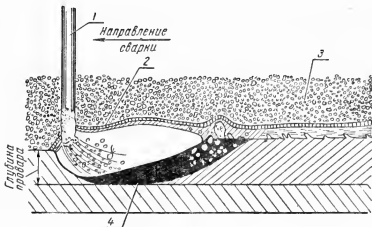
Схема образования сварочного шва под флюсом:
